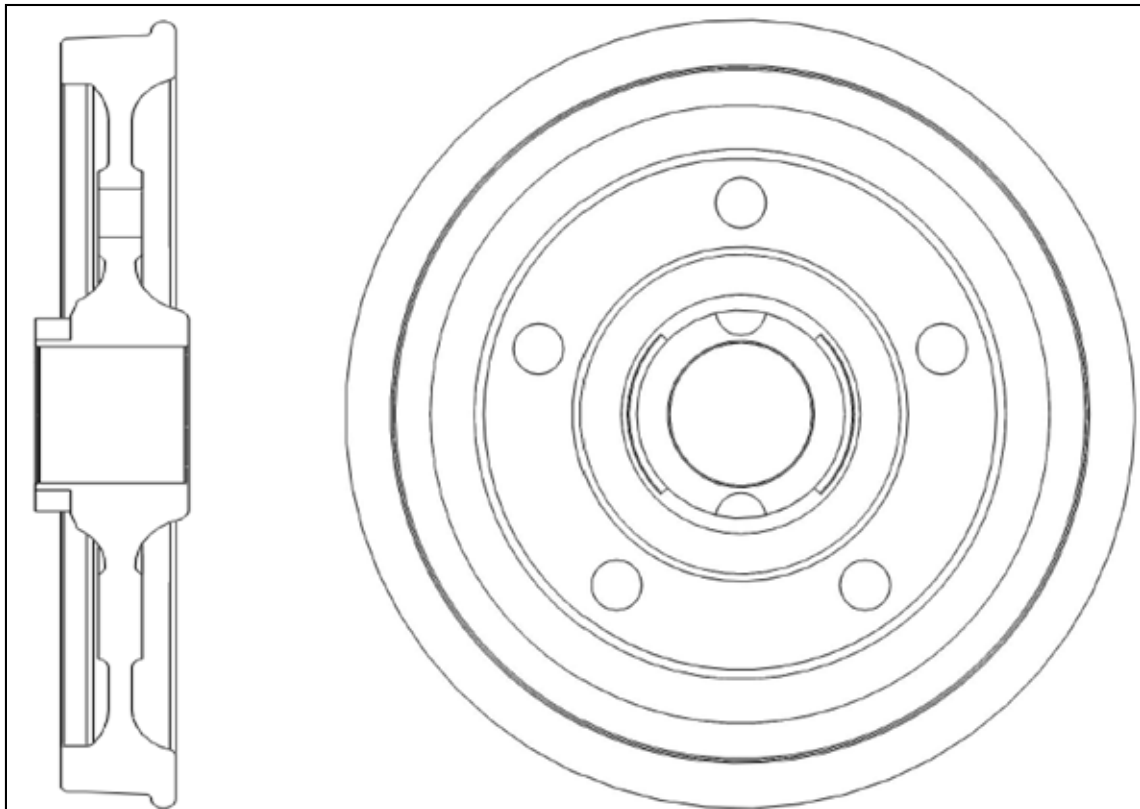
Vista del Corte de perfil y Alzado de la rueda.
